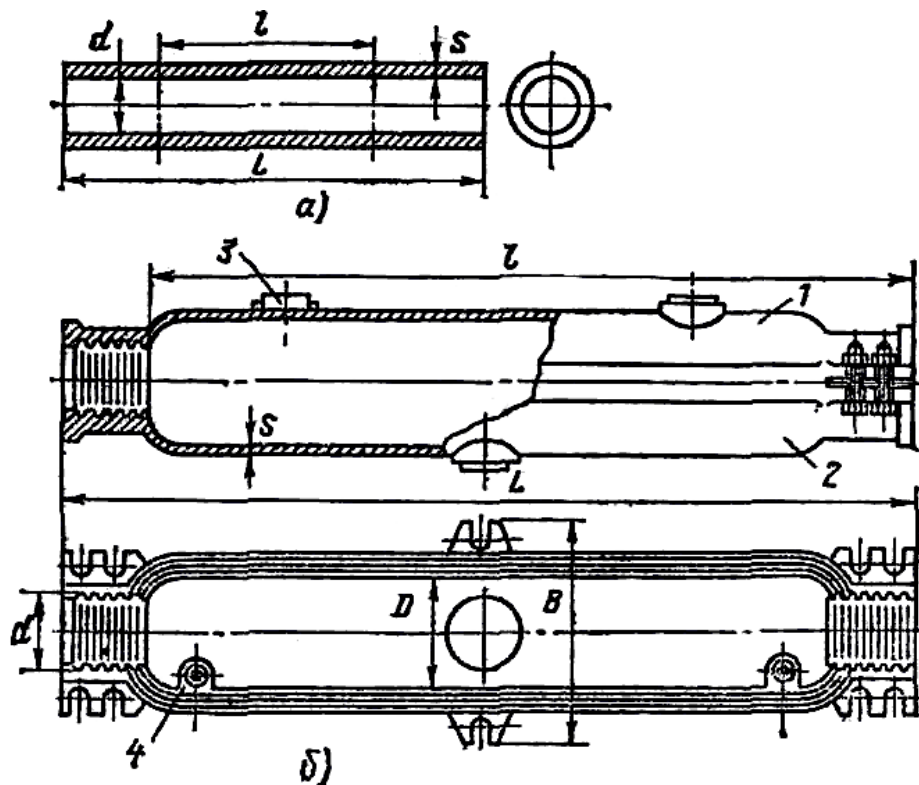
Свинцева труба для муфти (в) і кожух для муфти чавунний герметичний (б): 1— верхній напівкожух; 2 — нижній напівкожух; 2—пробка; 4— майданчик для заземлення.
